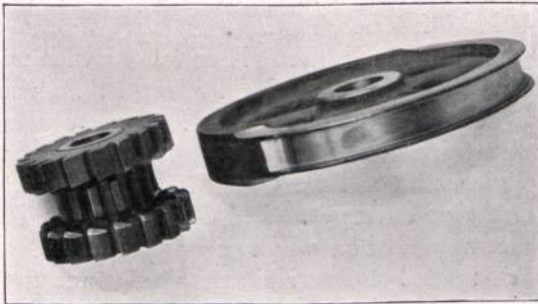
Fräser mit halbgefrästem Werkstück.
